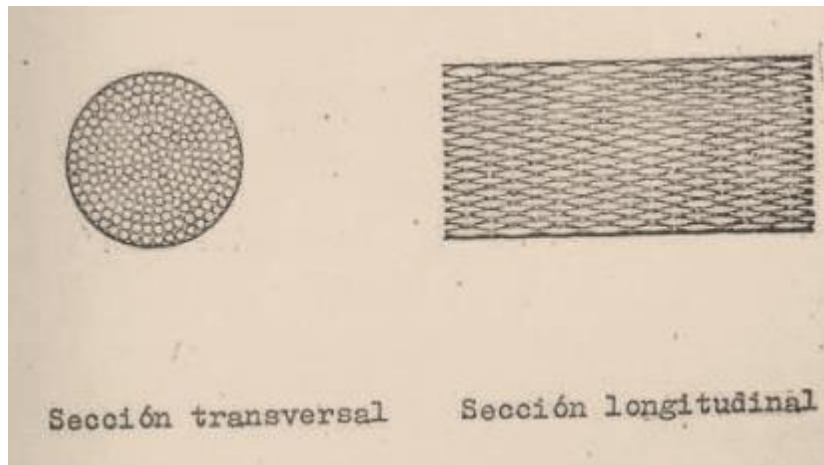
Sección transversal y sección longitudinal de la distribución interna de los granos del acero tras sufrir un estire y una reducción de sección del 75%.
